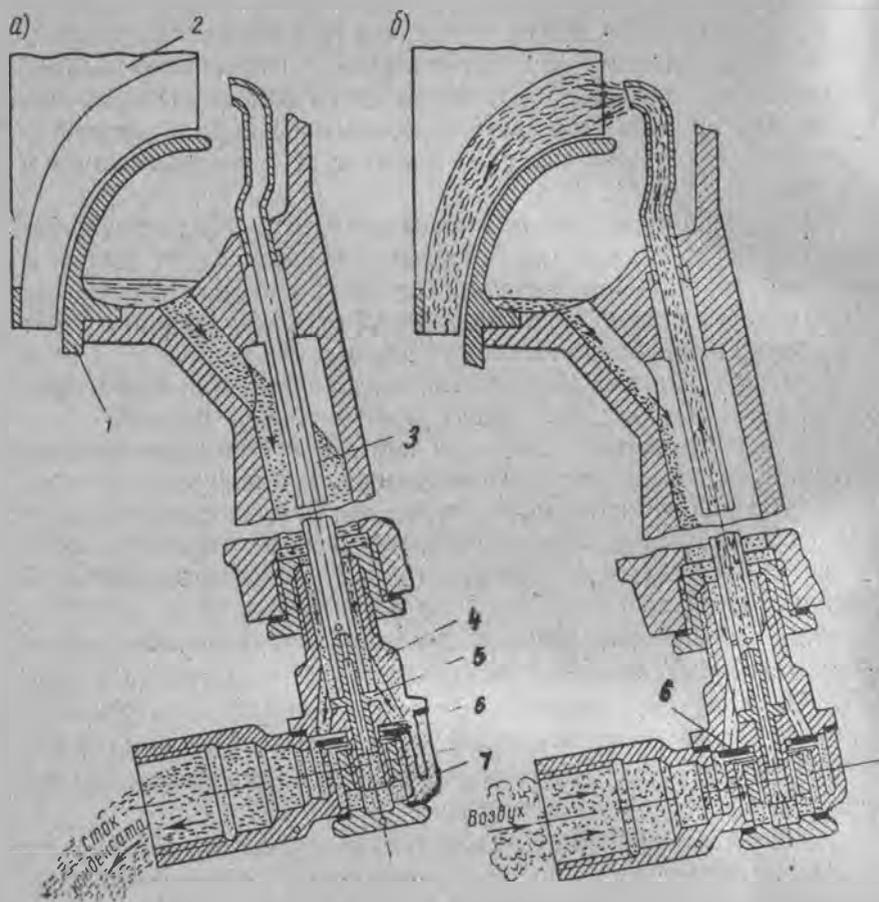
Схема устройства и работы комбинированного клапана нагнетателя: 1 — диффузор; 2 — крыльчатка; 3 — трубка; 4 — корпус; 5 — распылитель; 6 — подвижная шайба; 7 — ниппель
